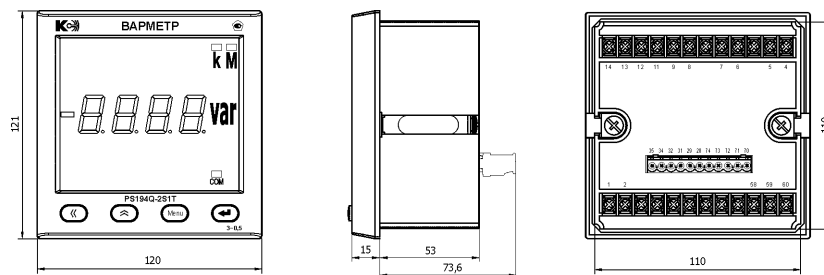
Внешний вид и размеры варметра PS194Q-2K1T-11001
